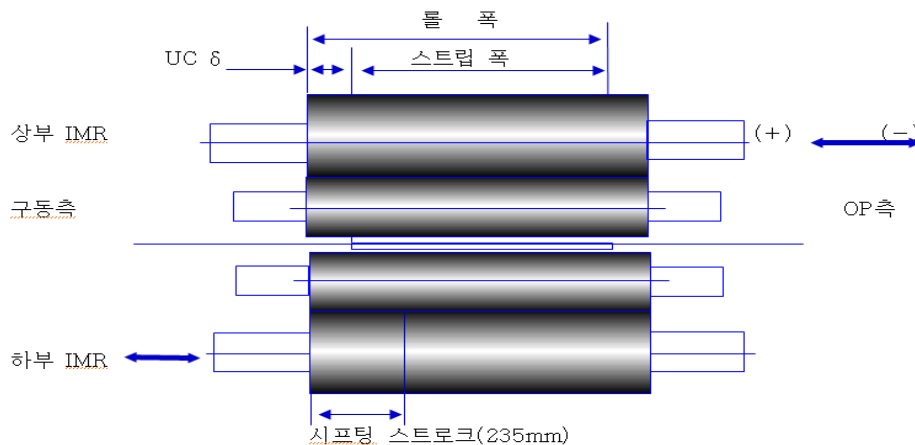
6단 압연기의 중간 Roll 형상 및 Shifting Adjustment
